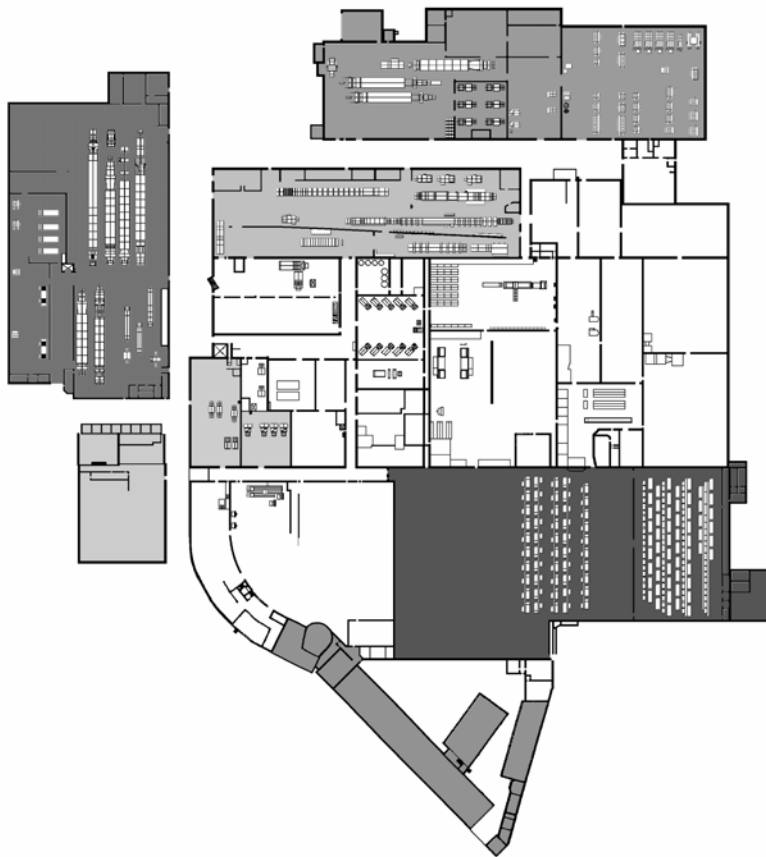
Beispiel: Lageplan eines Unternehmens
